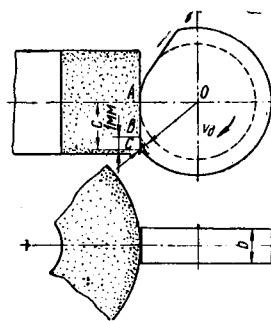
Схема расположения шлифовального круга и детали при обдирке цилиндрической поверхности круга.
